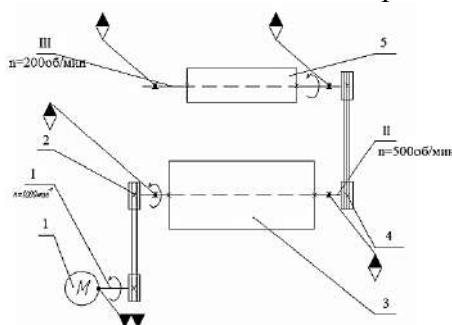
Совмещенная схема смазки вальцедекового станка: I – вал электродвигателя, II – вал рабочего вала, III – вал питающего вала. 1 – электродвигатель; 2, 4 – ременная передача; 3 – рабочий валок; 5 – питающий валок; 6 – деки.
